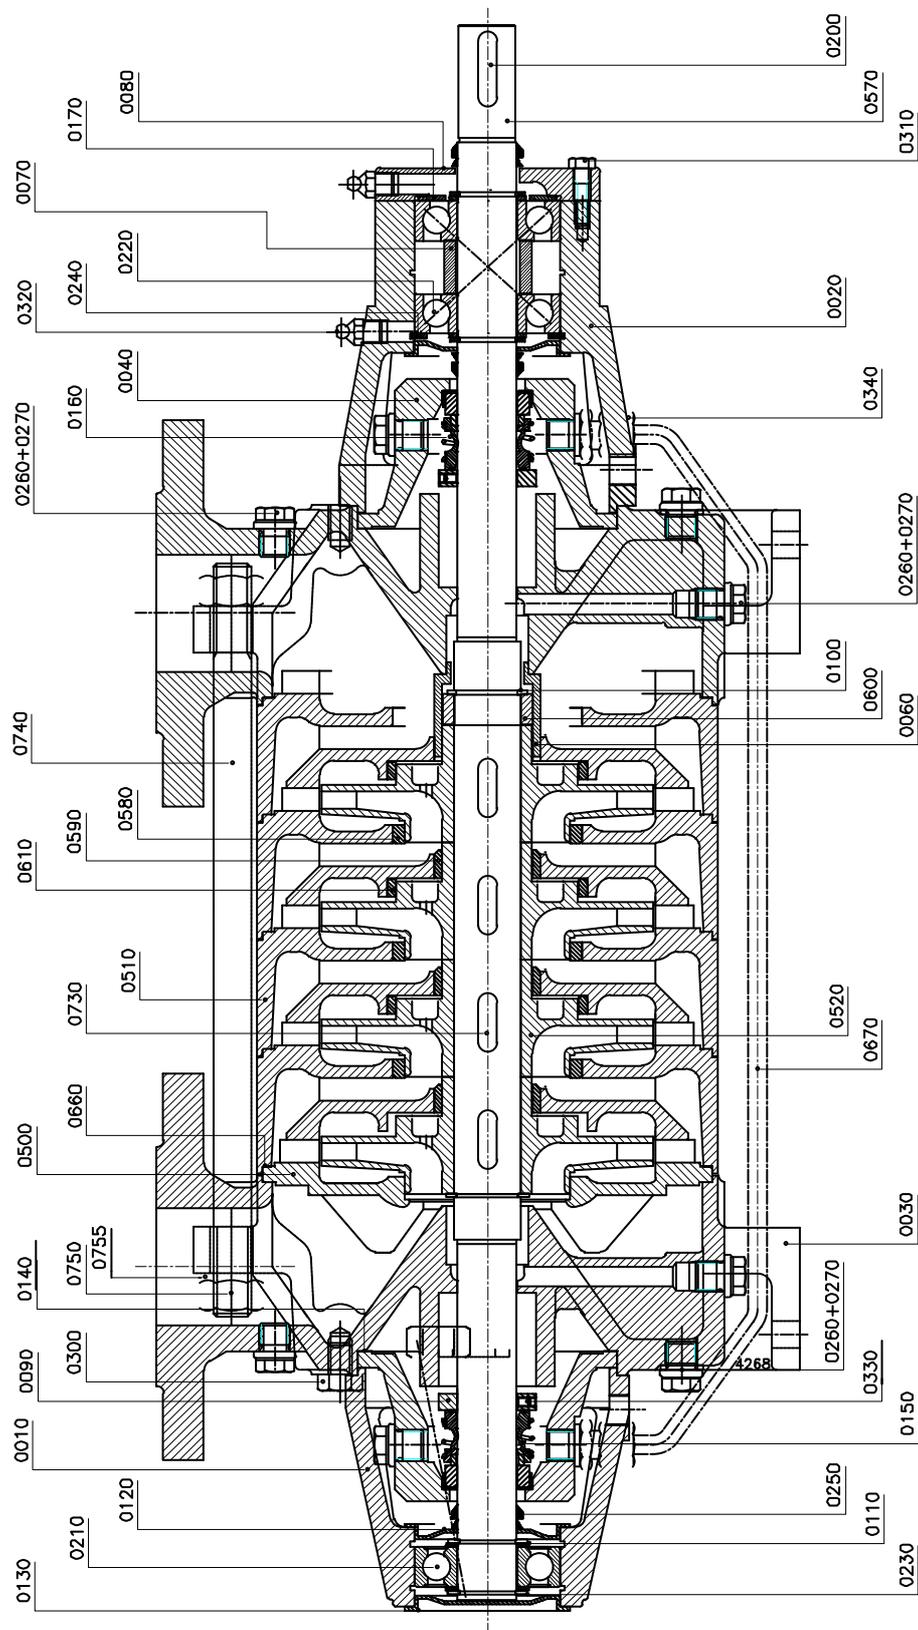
Модель MCHS 14a/b с подшипниками усиленной конструкции.
